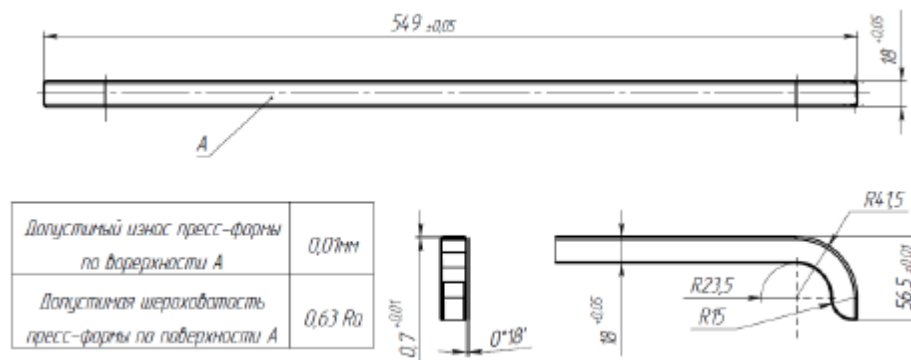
Ескіз ливарної деталі із ПКМ «Накладка»
